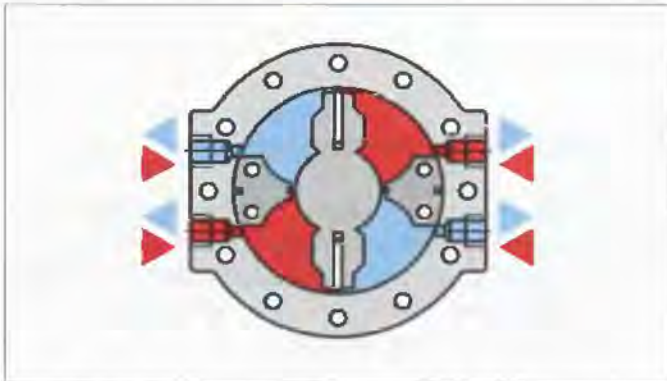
Двухлопастной поворотный гидродвигатель
